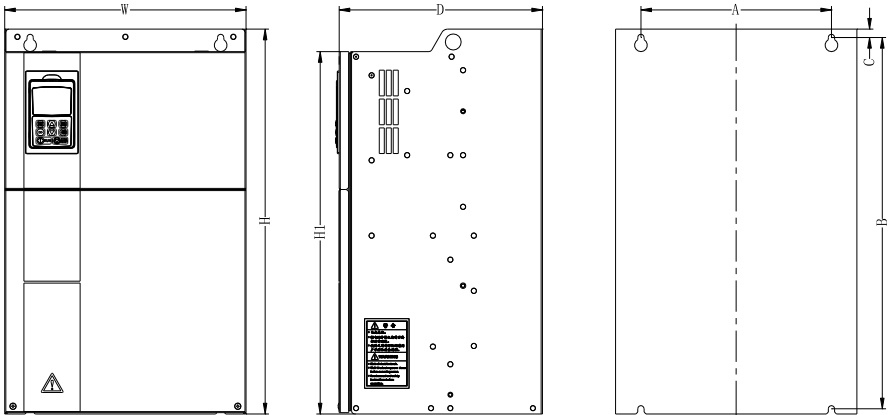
160~450kW 外型尺寸及安装尺寸示意图
